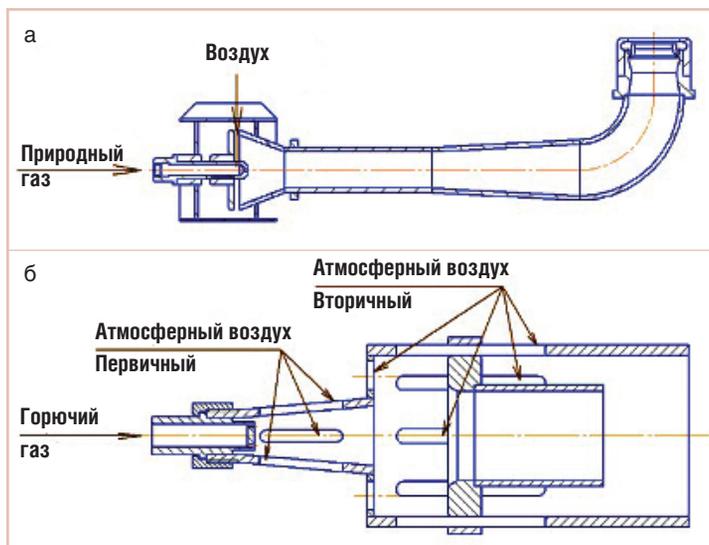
Газовоздушные горелки для разогрева 5-тонных сталеразливочных ковшей шиберного типа: а — ГВТ-15; б — ГН 53/3,9 М
